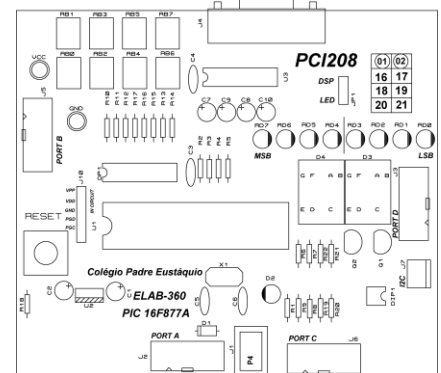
Layout da PCI lado solda, componentes e silk do módulo PIC16F877A em escala 1:2
